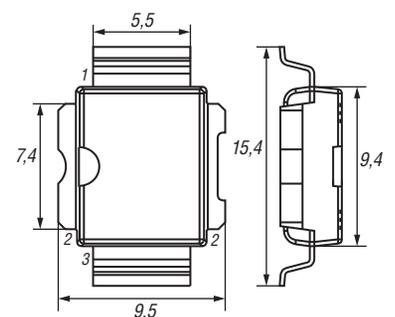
Pinbelegung und Abmessungen PowerSO-10RF gewinkelt
